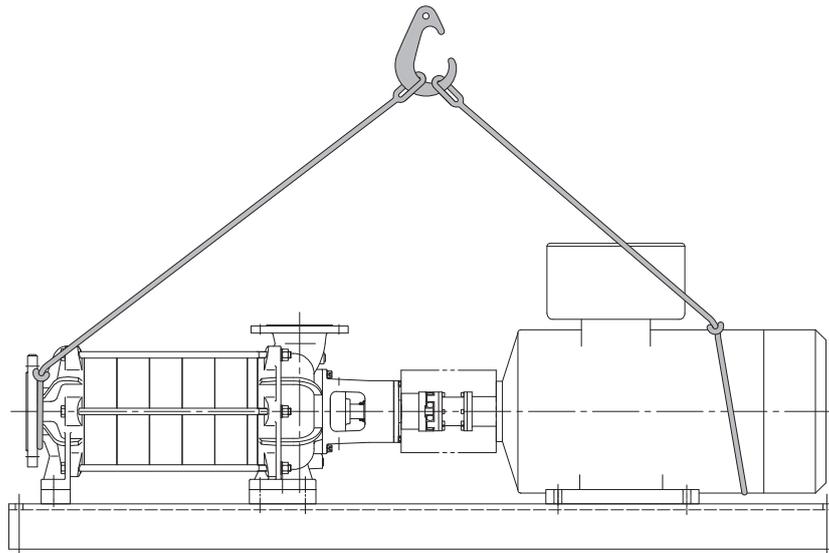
Pumpe mit Motor auf einer Grundplatte montiert
